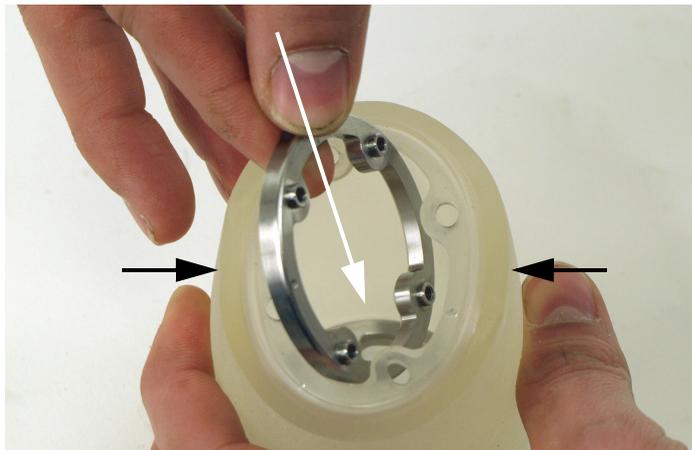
Entfernen des Edelstahlrings aus dem Rollenbelag
